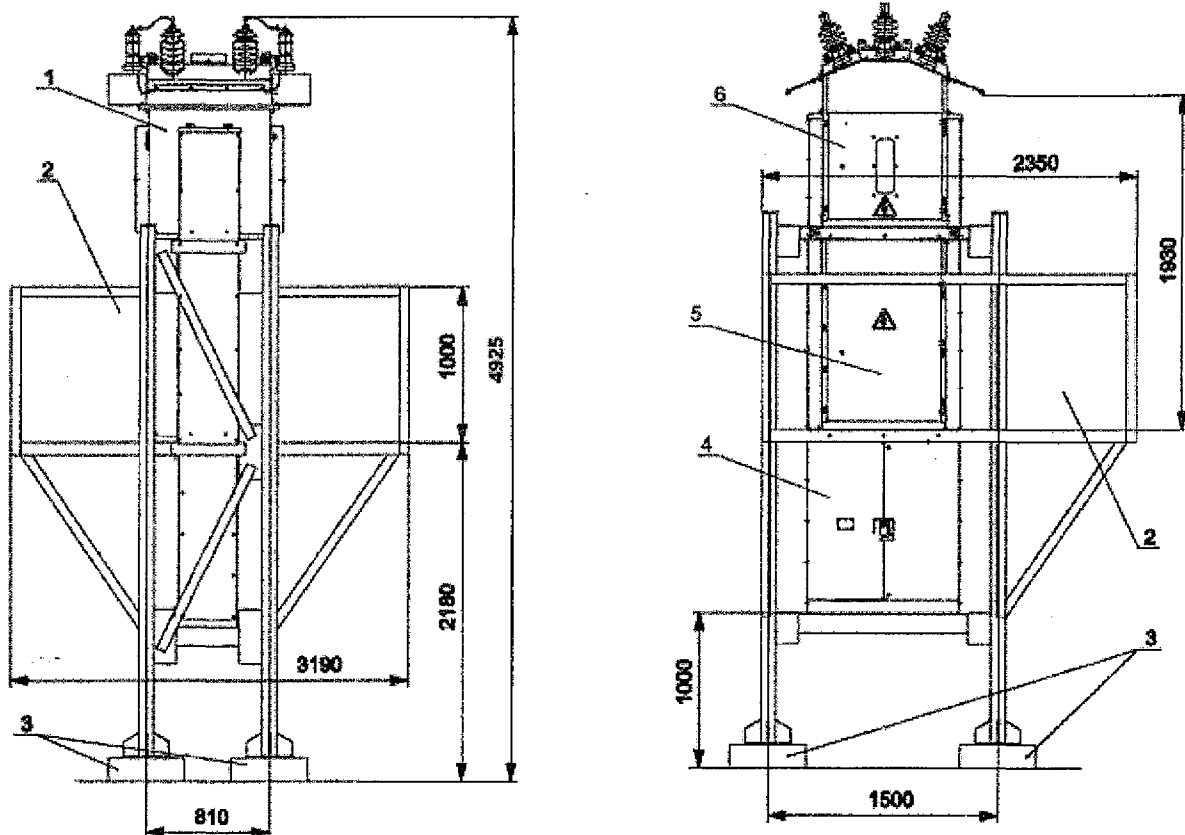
Общий вид и габаритные размеры устройства серии К-123
